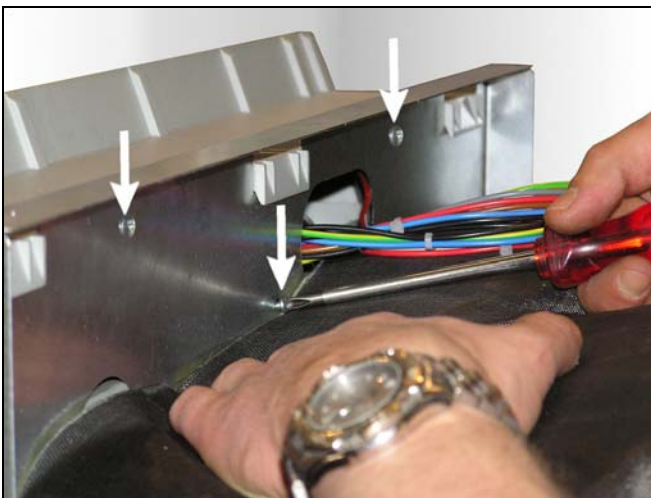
Befestigen Sie die Kesselschaltfeld-Konsole von der Rückseite des vorderen Verkleidungsbleches mit drei Blechschrauben.
